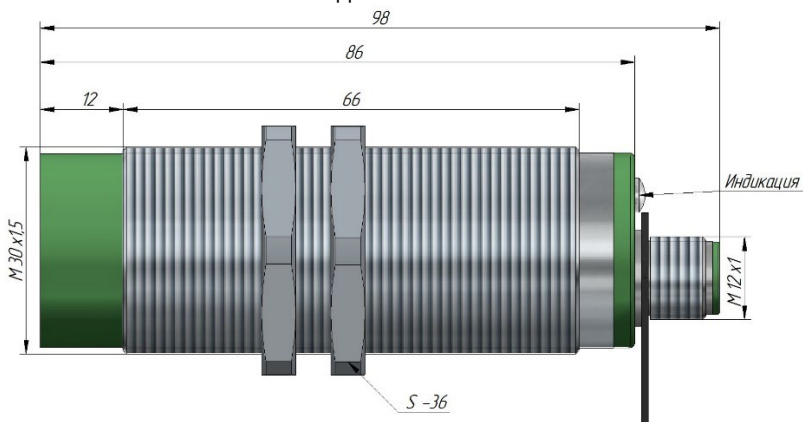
Внешний вид и габаритные размеры датчиков
